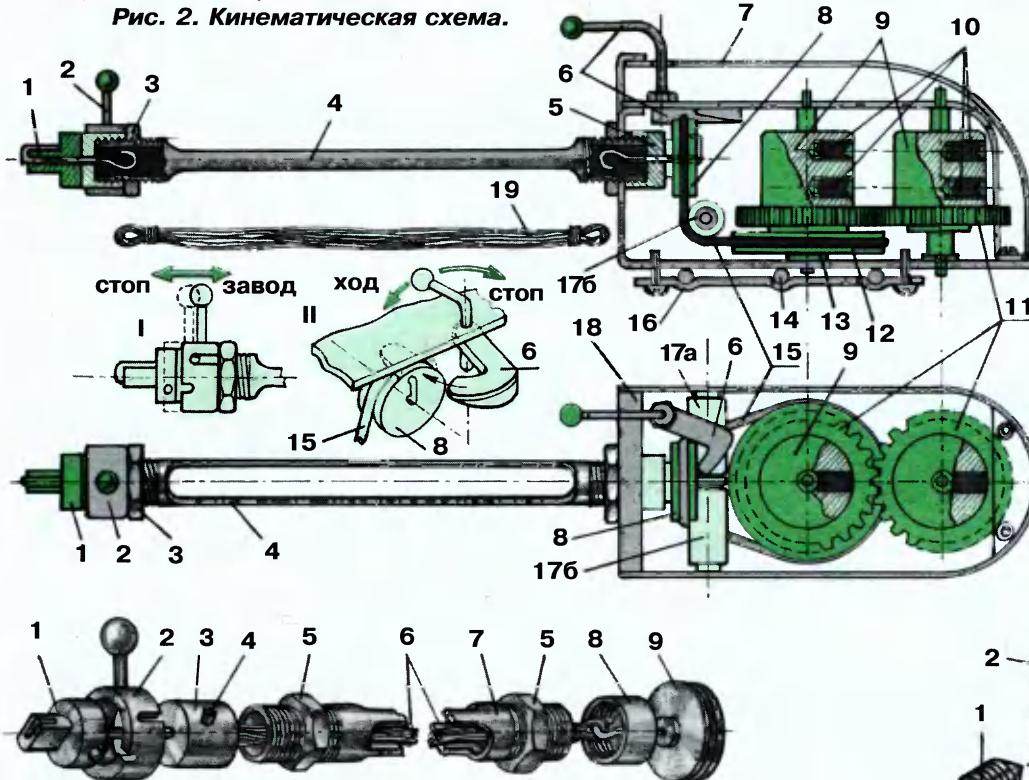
Компоновка узлов и конструкции модели: 1 — ось завода резиномотора; 2 — стопор оси завода; 3 — контргайка; 4 — консоль двигателя; 5 — втулка ведущего шкива; 6 — стопор ведущего шкива; 7 — обтекатель; 8 — ведущий шкив; 9 — диски разбалансировки (эксцентрики); 10 — грузики; 11 — шестерни; 12 — ведомый шкив; 13 — шайба; 14 — опора модели; 15 — пасник; 16 — платформа; 17 а, б — угловые ролики; 18 — картер; 19 — резиновый жгут.
